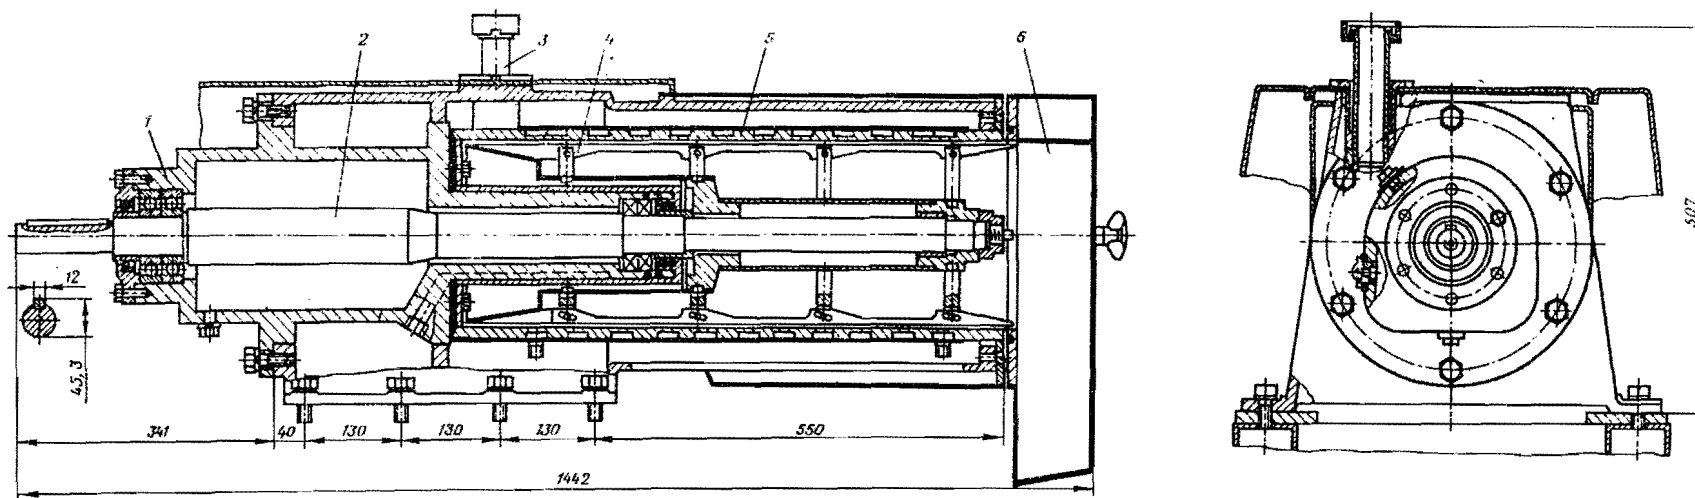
Общий вид сбивателя маслоизготовителя марки А1-ОЛО/1:
